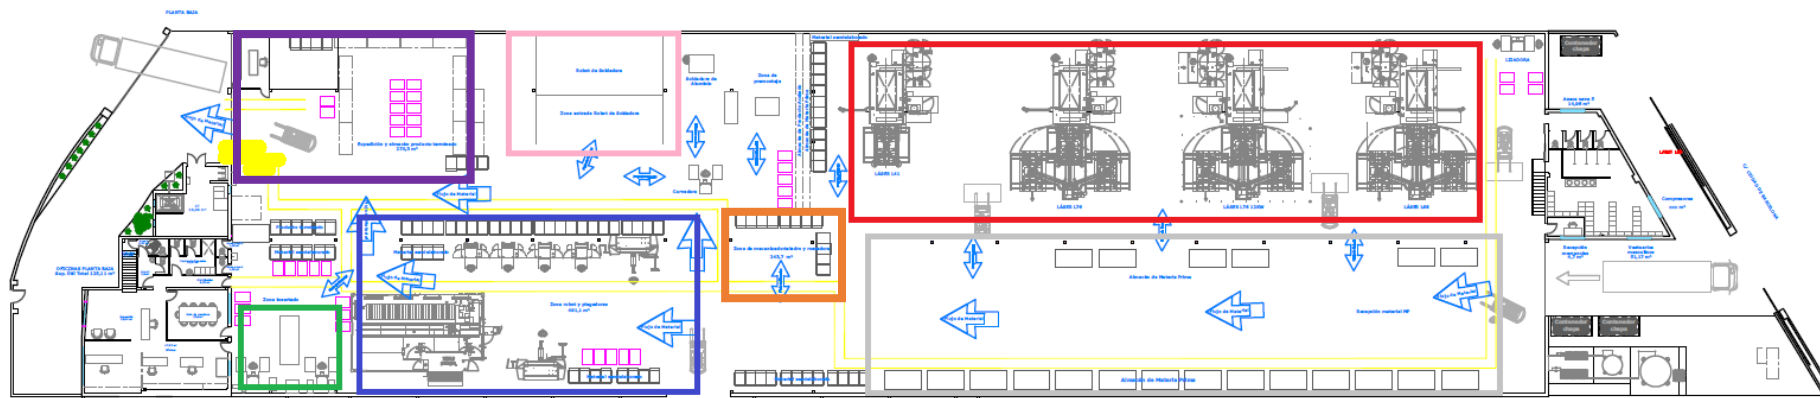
Lay-Out de planta principal de la empresa. Fuente: Archivo de empresa.
